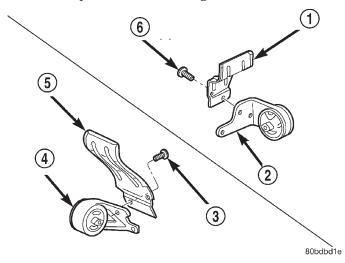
Desmontaje e instalación del protector contra del calor del soporte del motor
